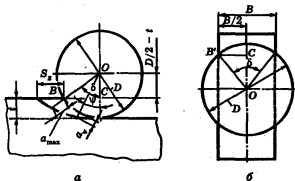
Угол контакта при фрезеровании: а — цилиндрической фрезой; б — торцовой
